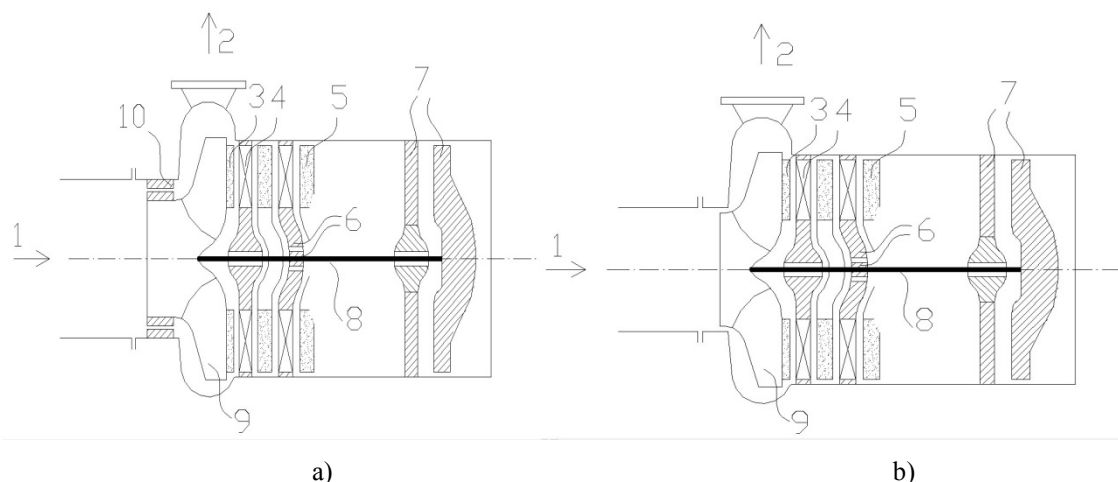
1 – sací potrubí; 2 – výtlak; 3 – ucpávka; 4 – mechanická spojka; 5 – elektromotor; 6 – ložiska; 7 – čerpadlo
